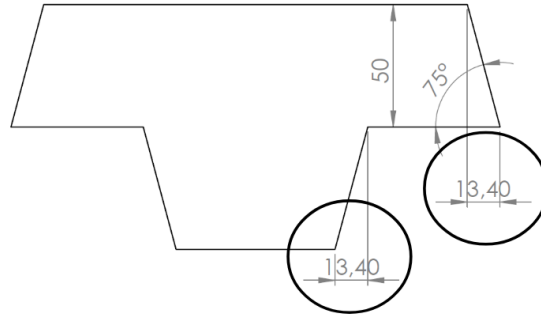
Tolérance insuffisante (si on exige 50mm) obtenue avec un angle de glissement fixée à 75° et une hauteur fixée à 50mm
